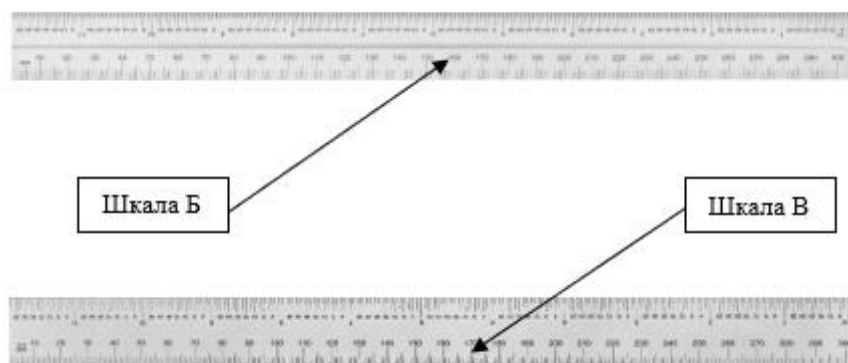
Общий вид шкал для измерения линейных размеров шаблона сварщика модели
